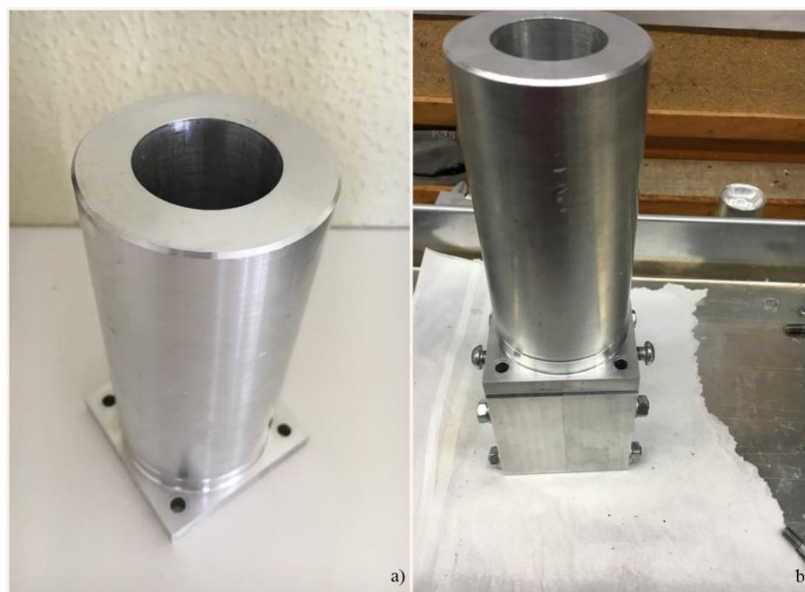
Sistema de enchimento do molde: a) Peça fabricada; b) Sistema de enchimento montado
